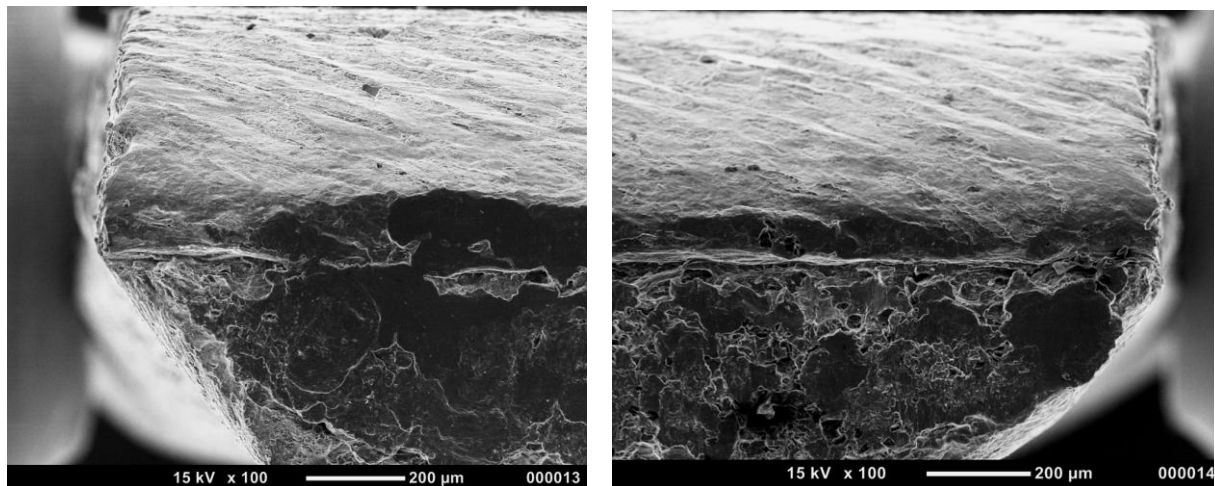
Übersichtsaufnahme der Bruchoberfläche einer Schweißung des Parametersatzes IMWF-33-00023 ($n=3000 \text{ min}^{-1}$, $v_x=500 \text{ mm/min}$)
